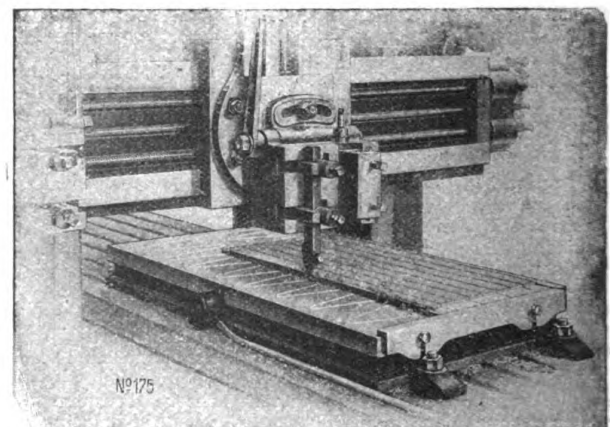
Magnetische Spannplatte auf einer Hobelmaschine.
